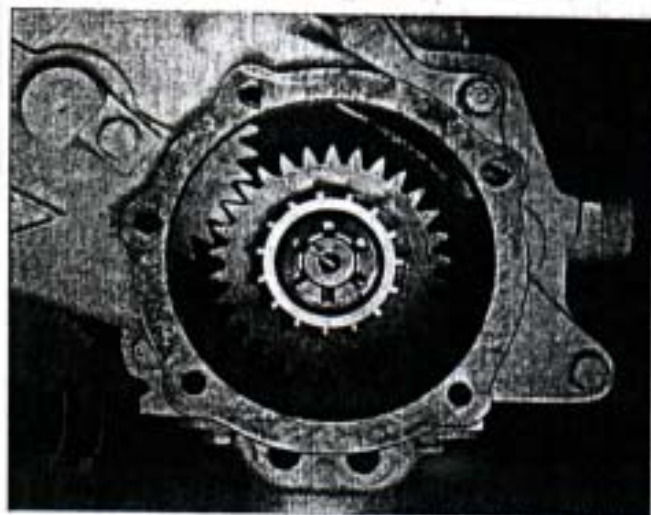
Detalle de la instalación del engranaje de mando de la caja de transferencia, acoplado en el engranaje intermedio.
